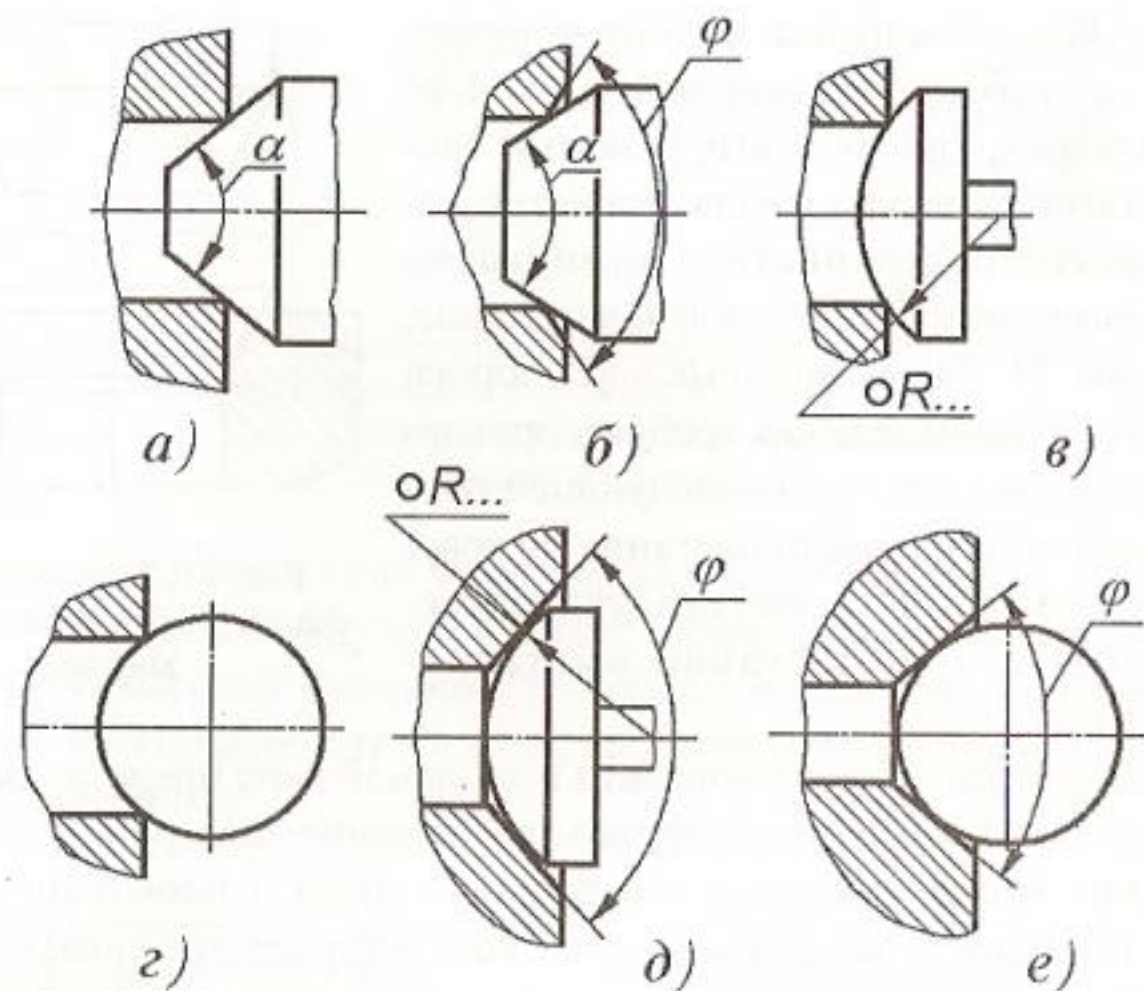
Конструктивные разновидности запорных пар типа «металл-металл» с линейным контактом
